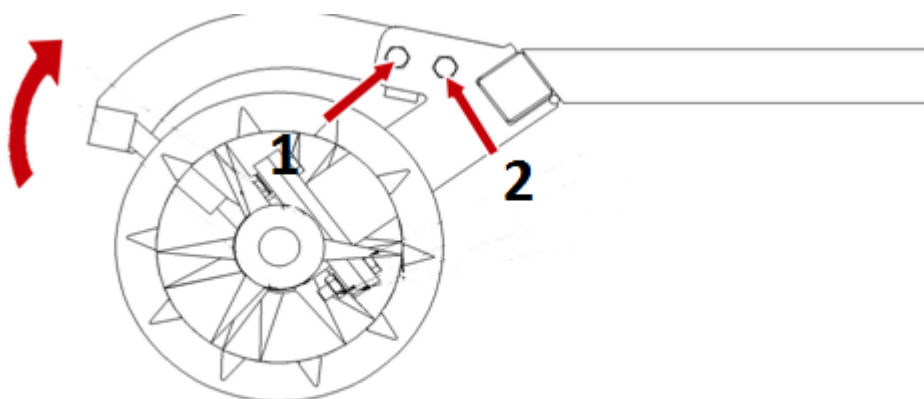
Durchbiegung des Stiftwellen-Reinigungskamms: 1; 2 - Kambefestigungsschrauben reinigen.
